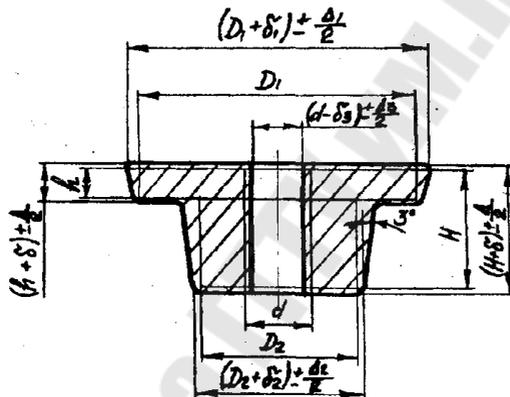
Схема назначения припусков и допусков для поковок 7-й группы
